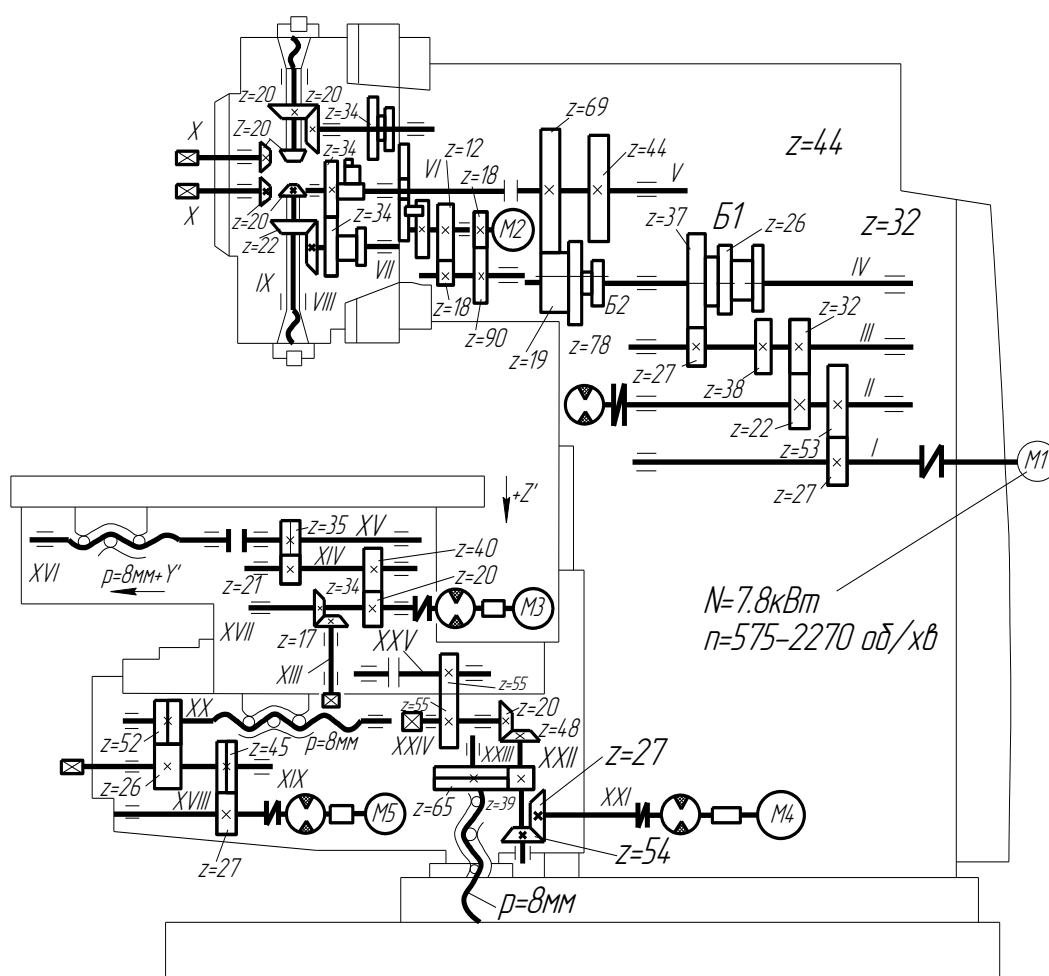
Кінематична схема вертикально-фрезерного консольного верстата з ЧПК моделі 6Р13Ф3
